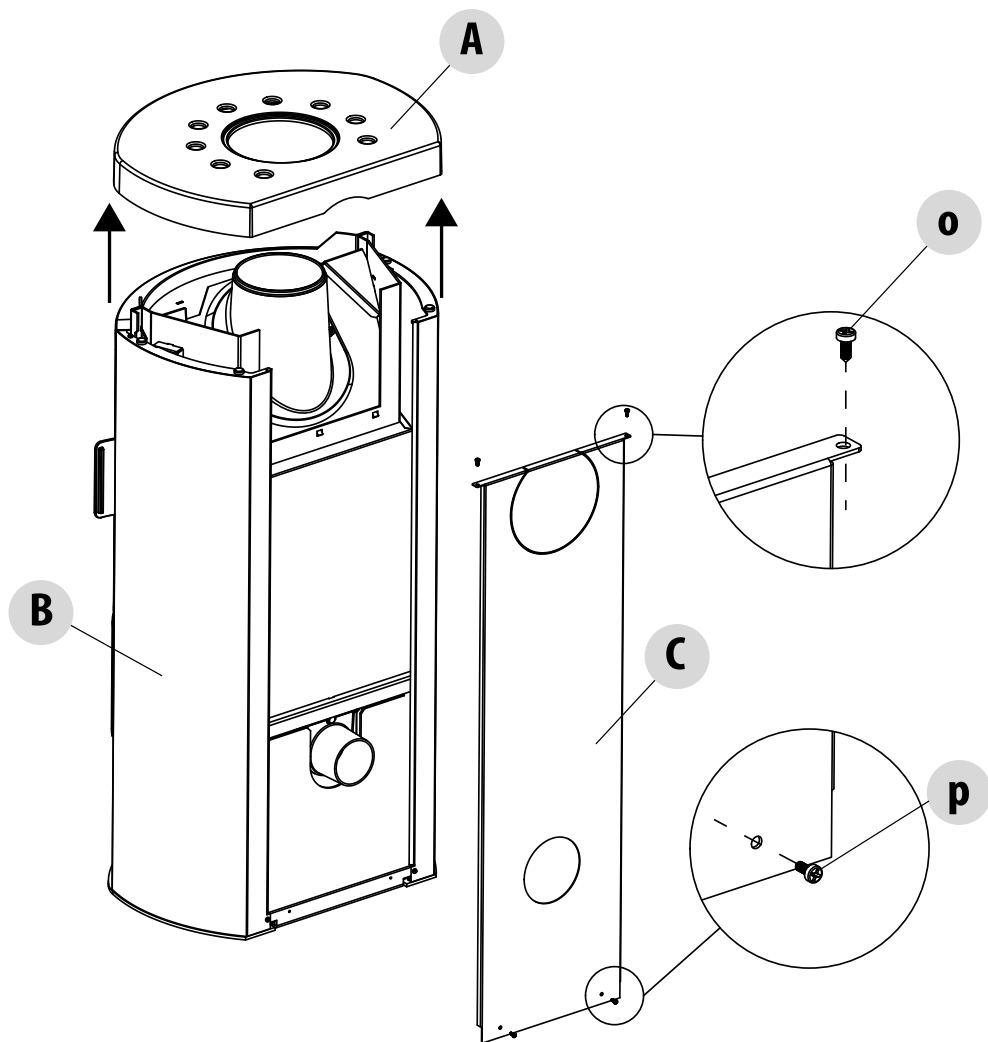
SMONTAGGIO TOP E PANNELLO POSTERIORE
